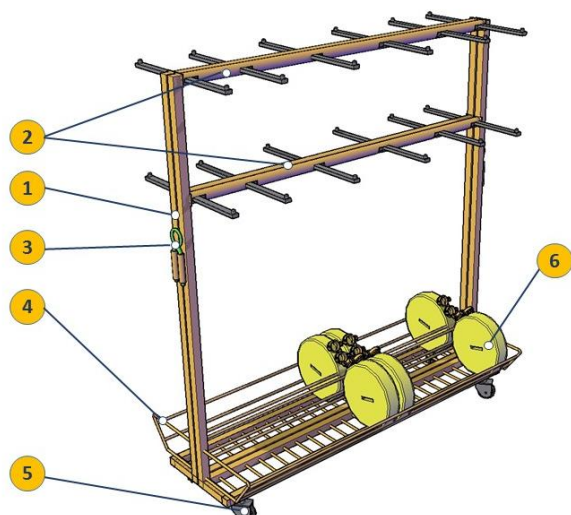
Стеллаж модульный для сушки и хранения пожарных рукавов: 1 – стойка; 2 – балка с поворотными консолями; 3 – «вилка» - соединитель; 4 – полка для хранения пожарных рукавов; 5 – колеса- роликовые с фиксатором; 6 – рукавная скатка
